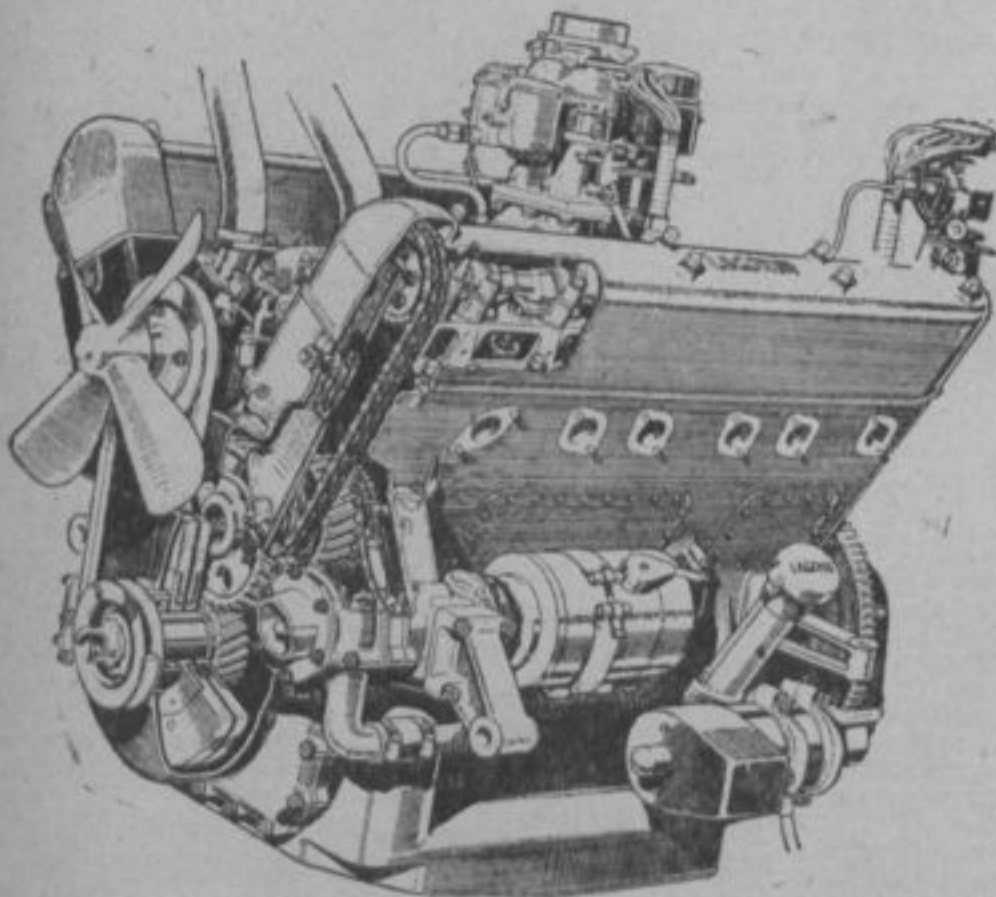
Общий вид с частичными размерами 12-цилиндрового двигателя «Лагонда»
